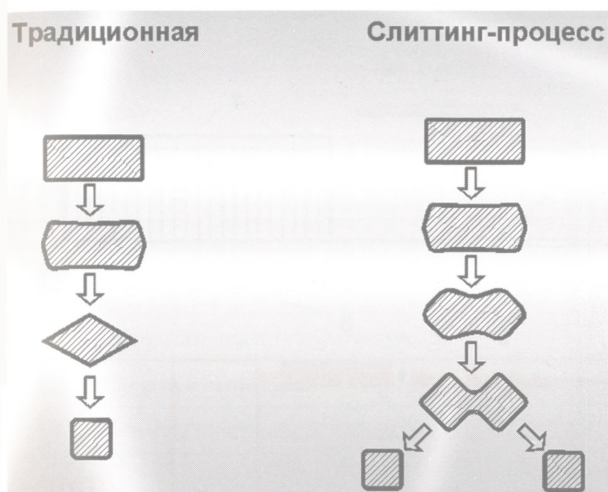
Схемы получения квадратной заготовки сечением 125 мм из бляма 250×300 мм
